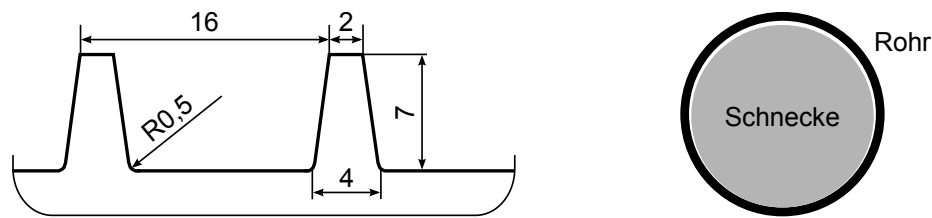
Links: Abmessungen der trapezförmigen Gewindestege der Extruderschnecke im Querschnitt. Rechts: Schematische Querschnittsdarstellung des Spaltes zwischen Schnecke und Zylinderwand.
